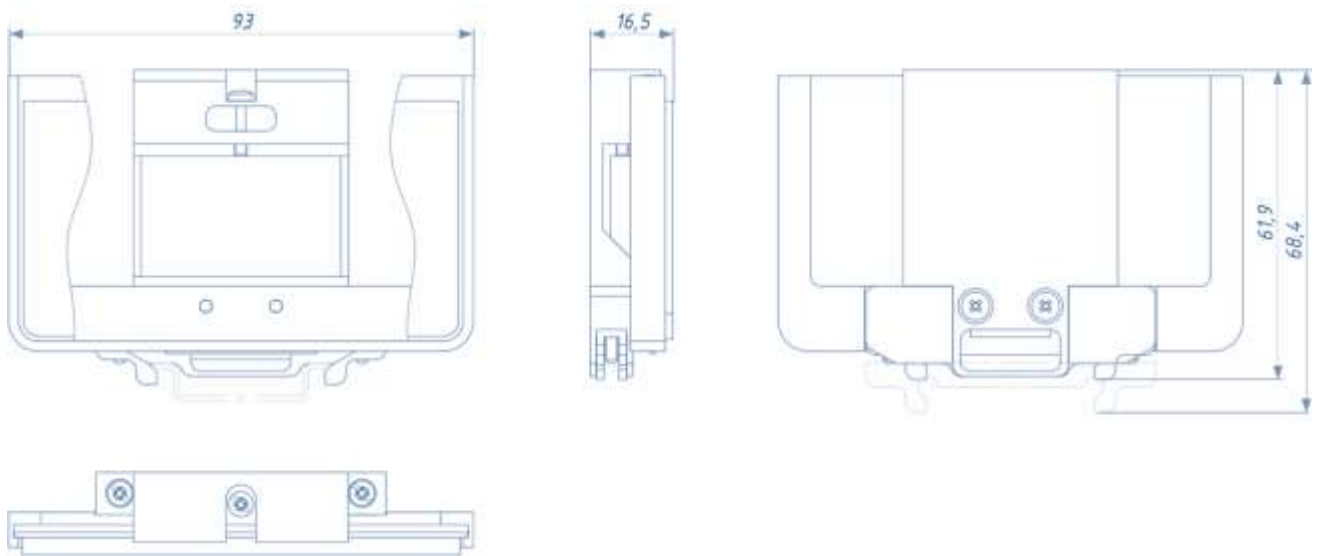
Габаритные размеры держателя концевого из комплекта ACS00098-01
